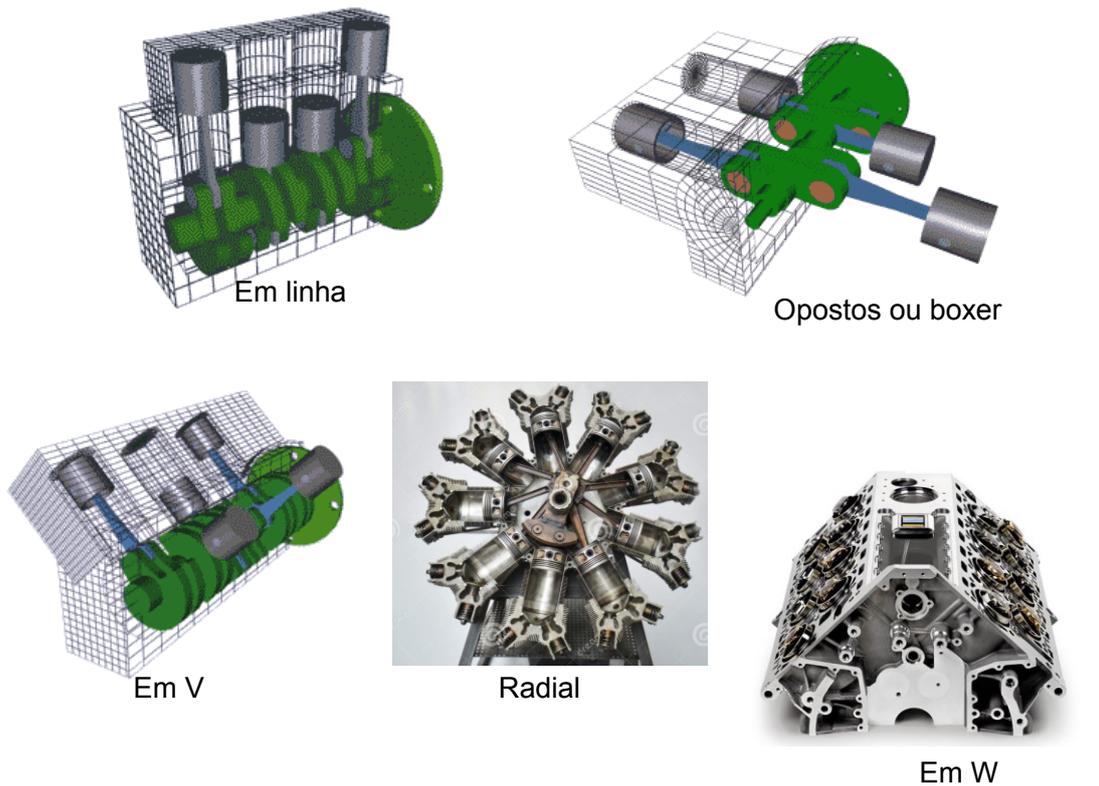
Tipos de disposição de cilindros em motores de movimento alternativo.
